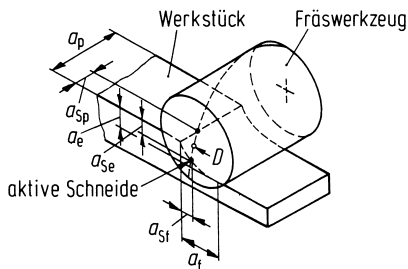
Eingriffsgrößen des Werkzeuges und der Schneide beim Umfangsplanfräsen (nach DIN 6580)
